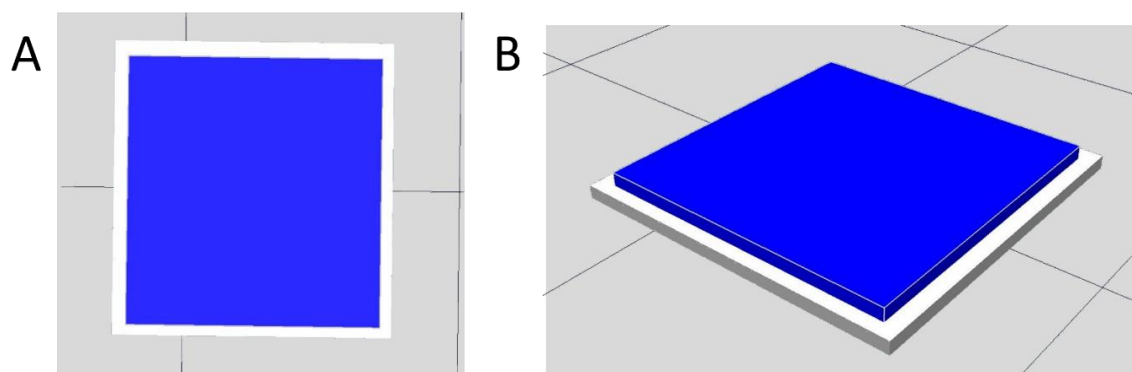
Modèle généré via Autodesk pour imprimer la 2^{de} couche (A) vu d'en haut ou (B) vu en perspective.
